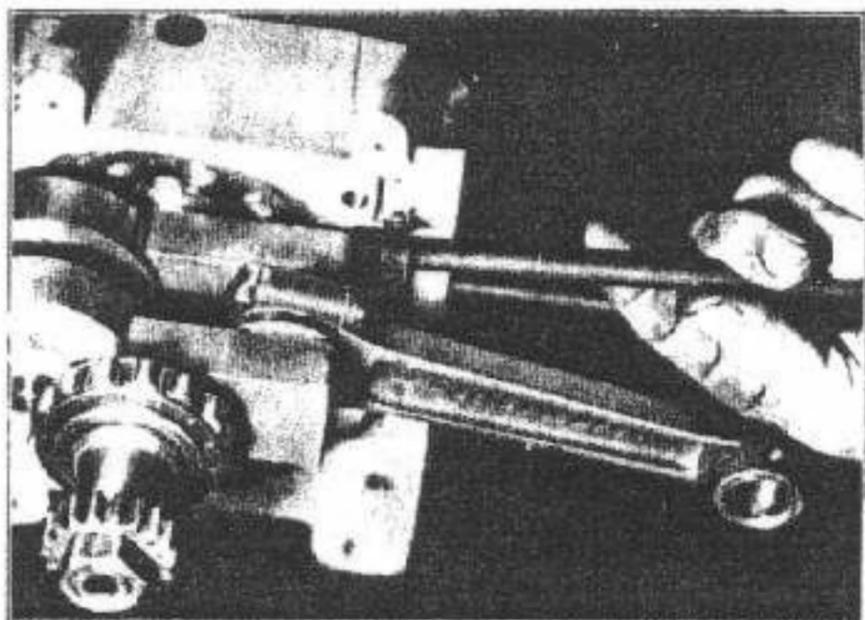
Prima di chiudere i due mezzi carter ricordare di piazzare il tirante per fissaggio testa e cilindro.
